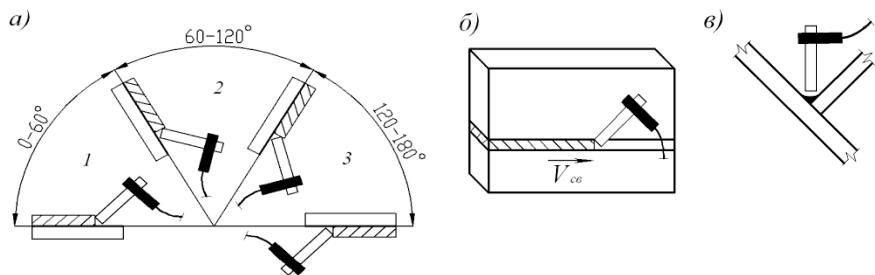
Положение сварных швов в пространстве:
